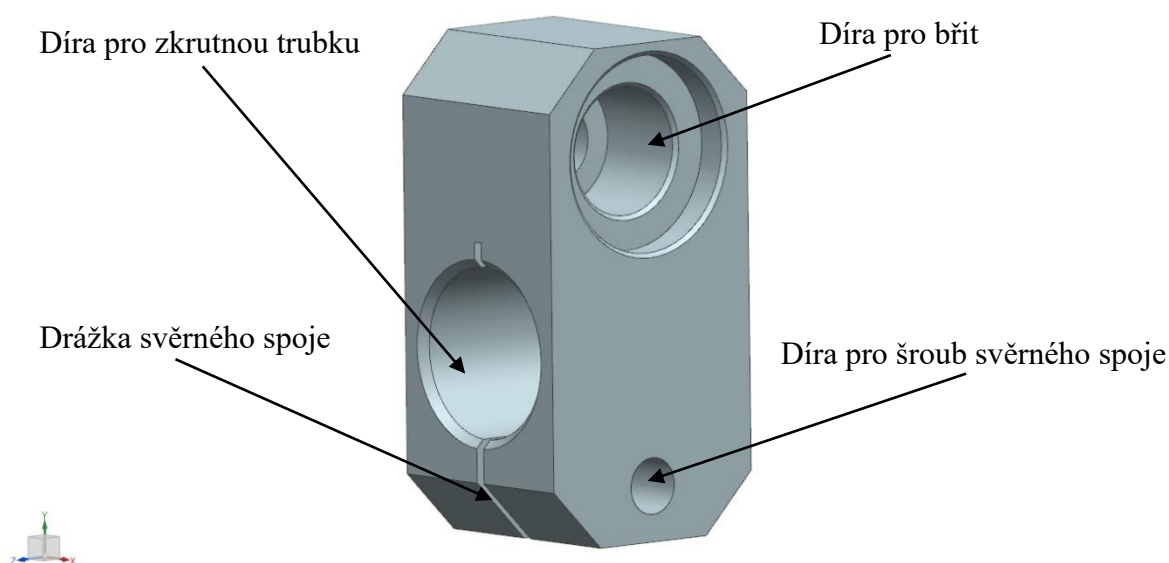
Řez držákem zadního stabilizátoru (úprava trubky)
